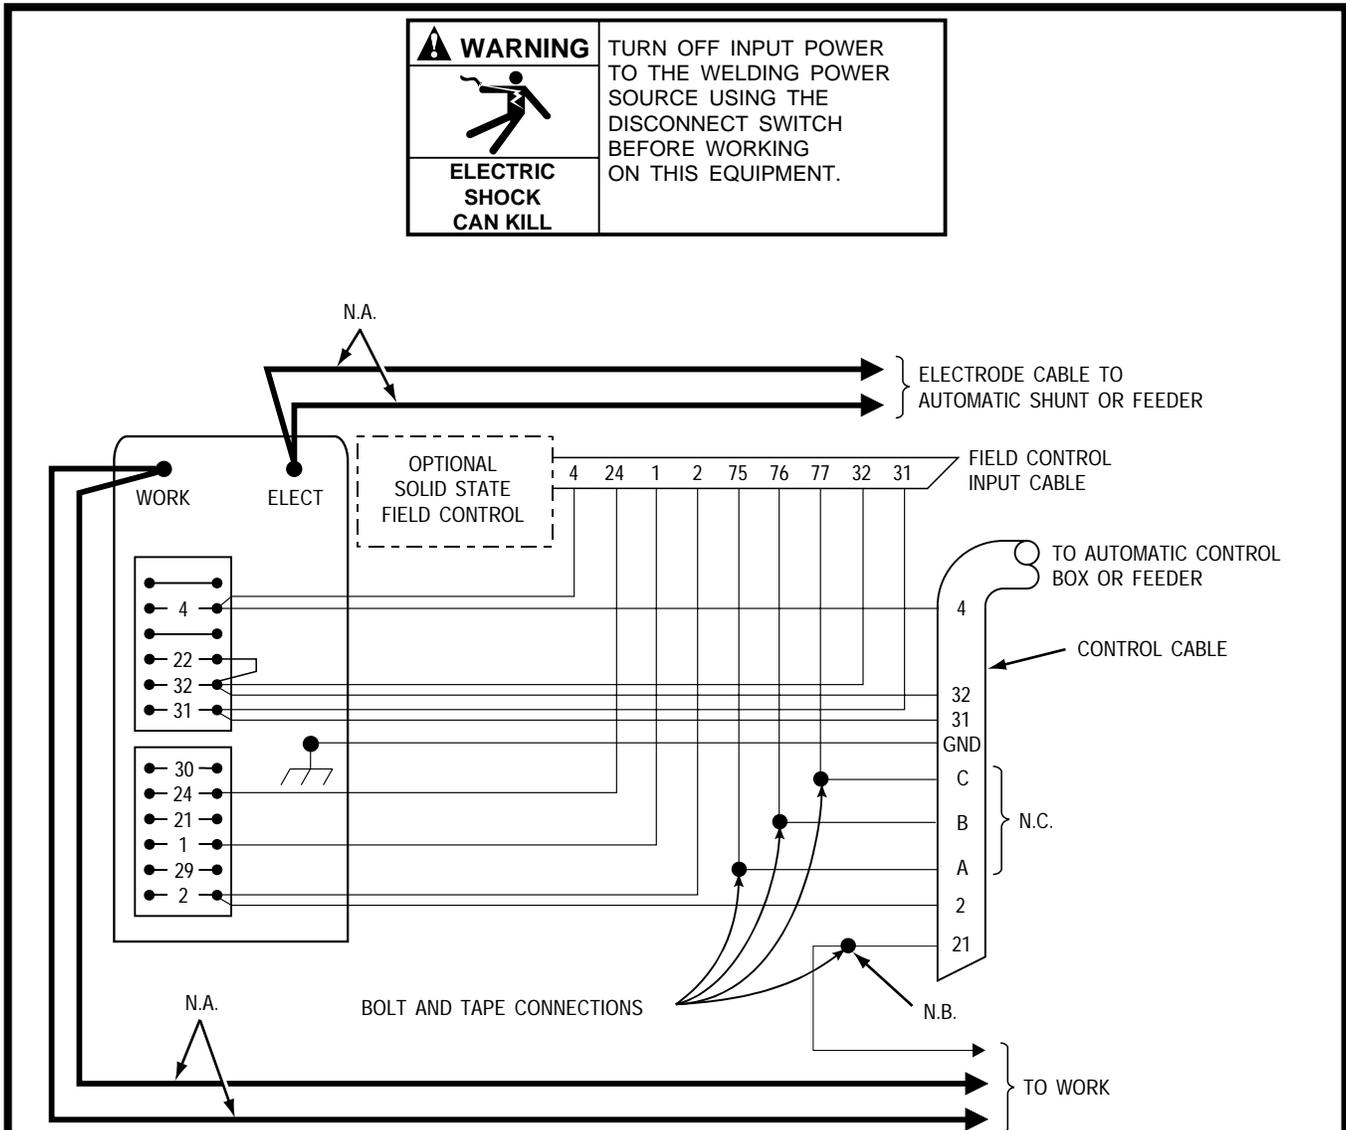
CONEXIÓN DE NA-3 (TODAS) A UN GENERADOR SAM O A UN EQUIPO DE SOLDADURA ACCIONADO POR MOTOR.
